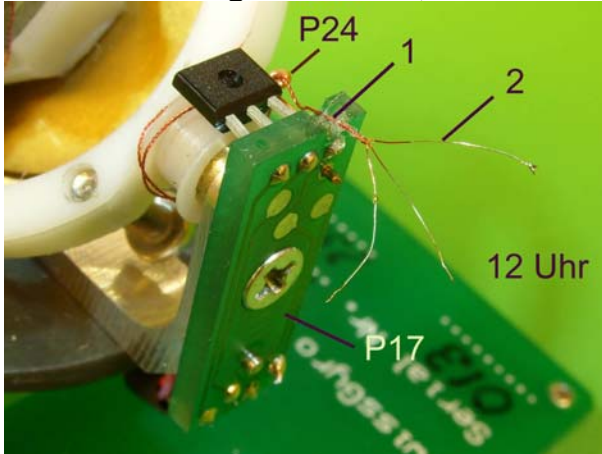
Kardan 60 Grad kippen, Kabel in Nut (1) von Seitenprint P17 kleben. Drähte (2) kürzen und entdrillen, Isolation bei 350 Grad entfernen.
